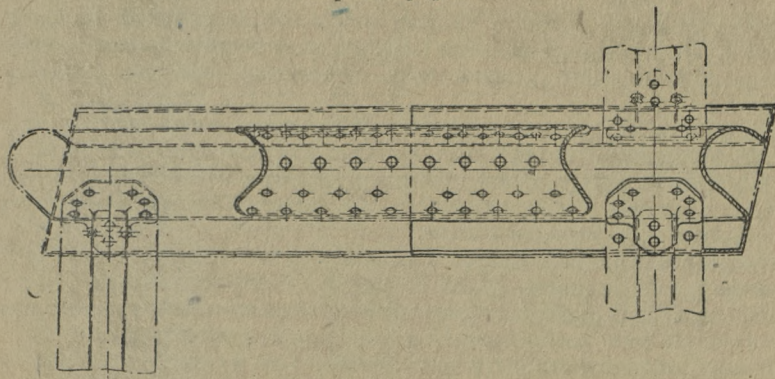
а. Накладка на профильный лонжерон, охватывающая выступающую часть профиля
